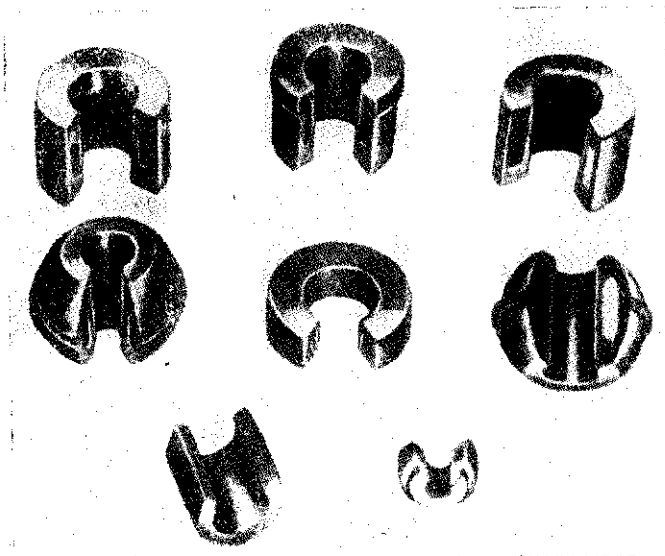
Различные конструкции спеченных подшипников скольжения с резервуарами для масла (Галлер)
